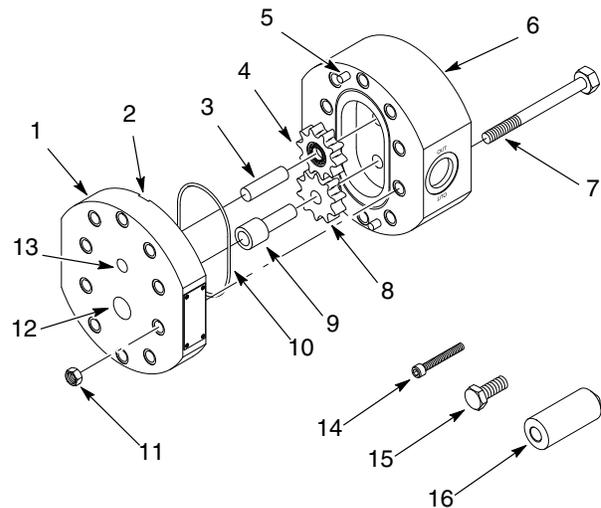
Typischer Durchflussmesser mit eingepresster Welle
